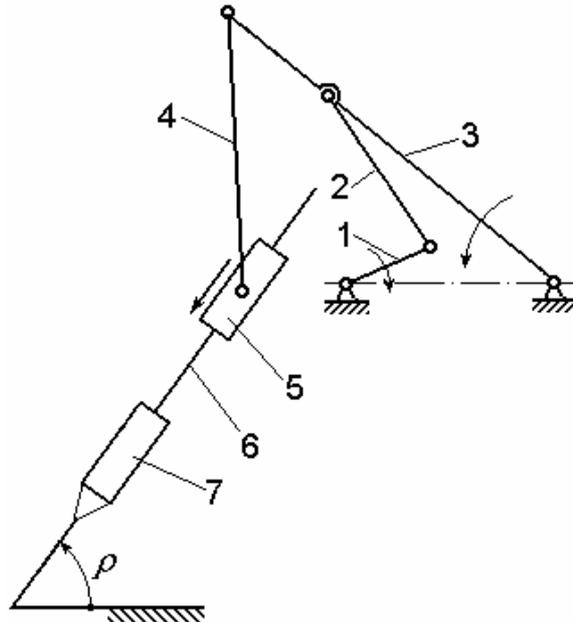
Шестизвенный шарнирно-рычажный ударный механизм:
